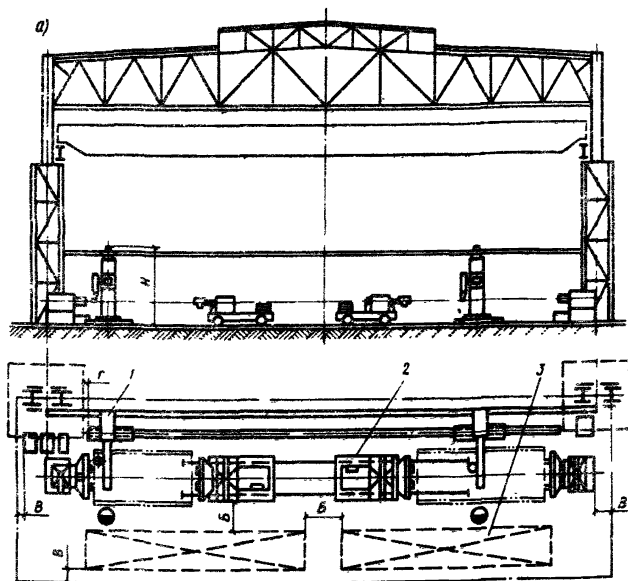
Размещение поточной линии сборки, сварки и резки стержней двутаврового сечения.
